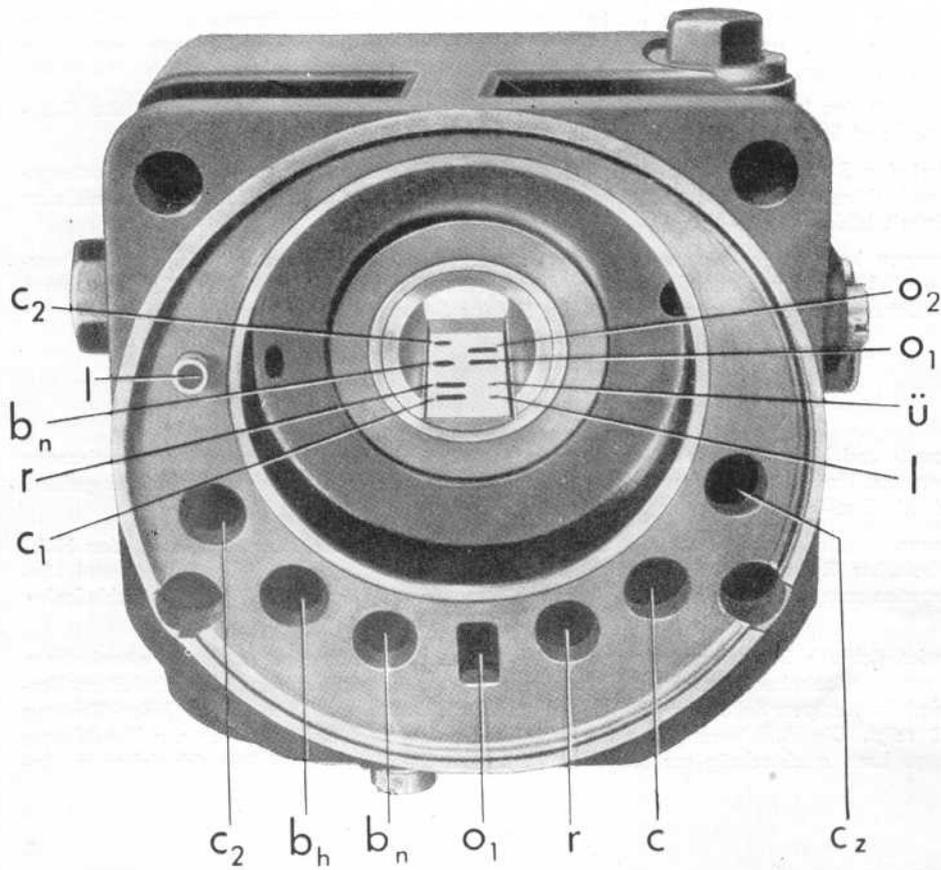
Blick auf den Schieberspiegel im Gehäuse des Hauptsteuerventils
